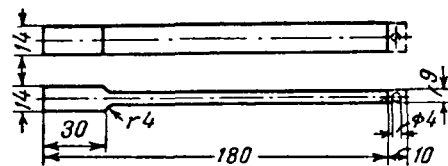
Вид и размеры образцов для испытания высоковольтного фарфора на знакопеременный симметричный изгиб.
